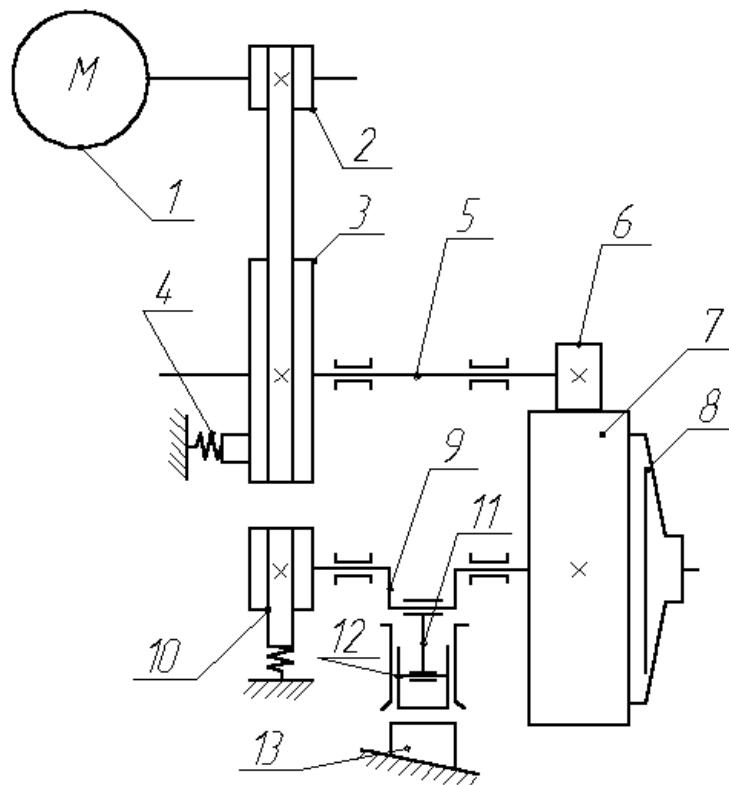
Кинематическая схема кривошипного пресса:
